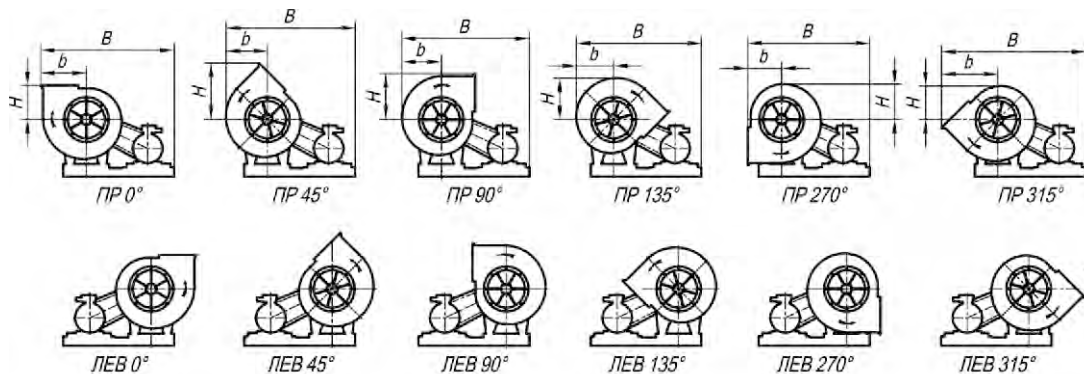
Положения корпуса вентилятора ВР 9-55 исп-5.
